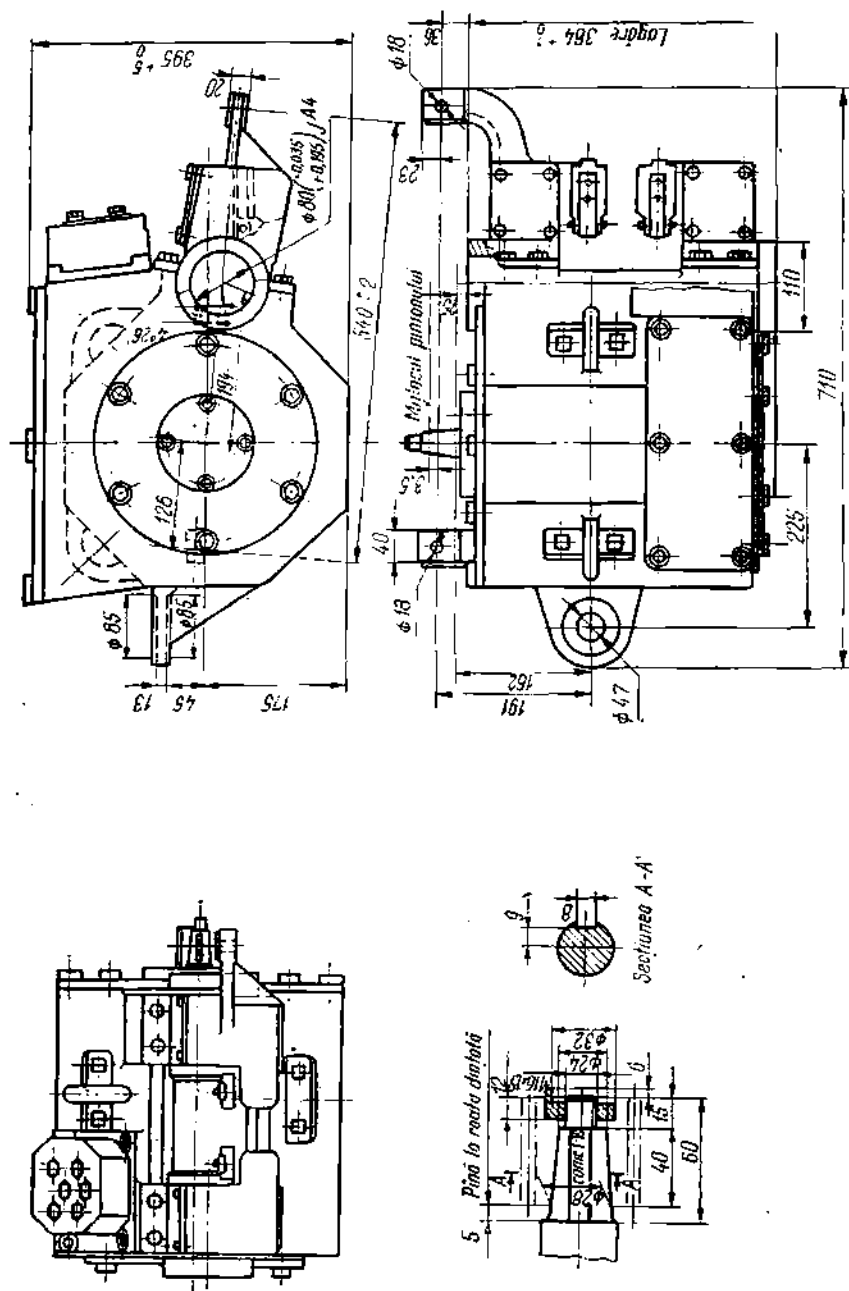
Motor tip SSTA 5,2-72. Dimensiuni de montaj.
